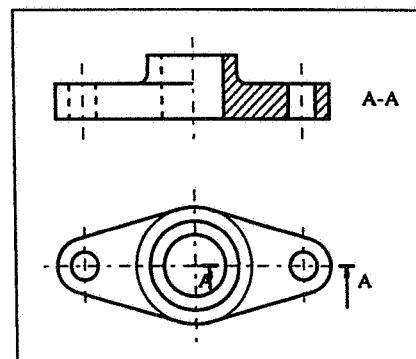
Rappresentazione in pianta e con semisezione di un pezzo dotato di simmetria.
